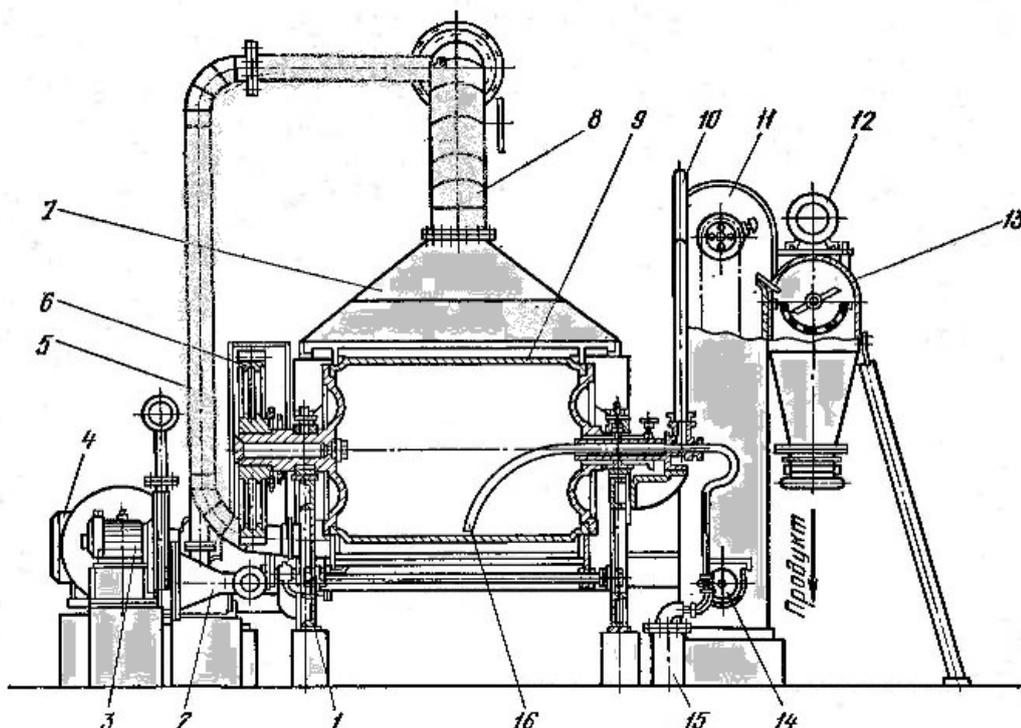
Вальцовая атмосферная сушилка: 1 - станина; 2, 5 - воздуховоды; 3 - электродвигатель вентилятора; 4 - электродвигатель вальцов; 6 - приводной механизм; 7 - вытяжной зонтик; 8 - устройство для отвода паров; 9 - вальцы; 10 - патрубок для входа пара; 11 - элеватор; 12 - электродвигатель дробилки; 13 - дробилки; 14 - шнек; 15 - конденсатоотводчик; 16 - патрубок для отвода конденсата
